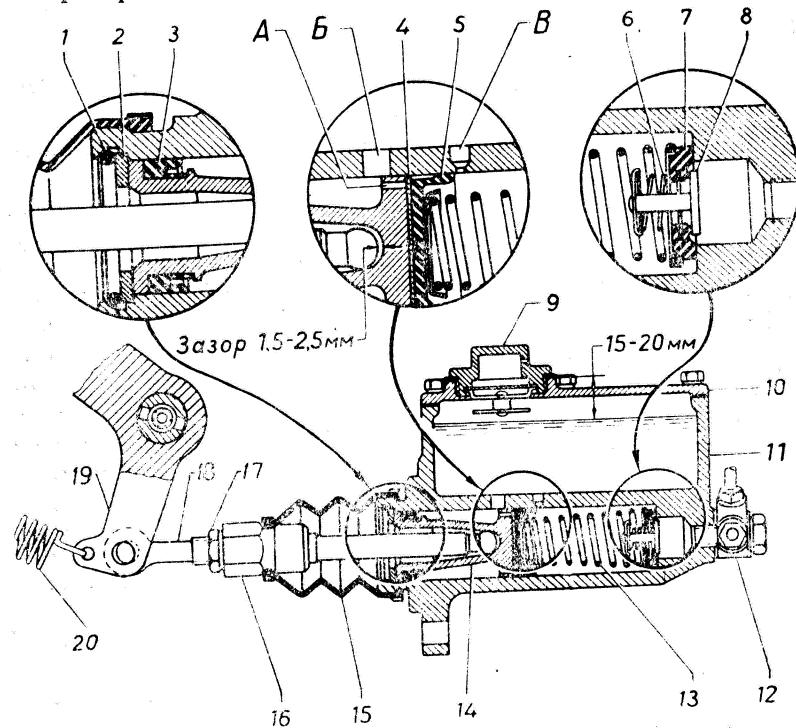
Главный цилиндр гидравлического привода тормозов.
